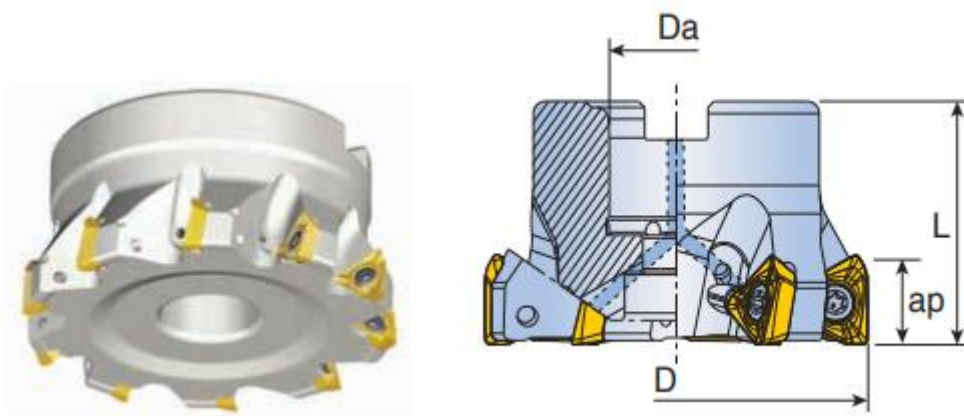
Торцева фреза Mill Rush 33 TF90 фірми Taegutec
